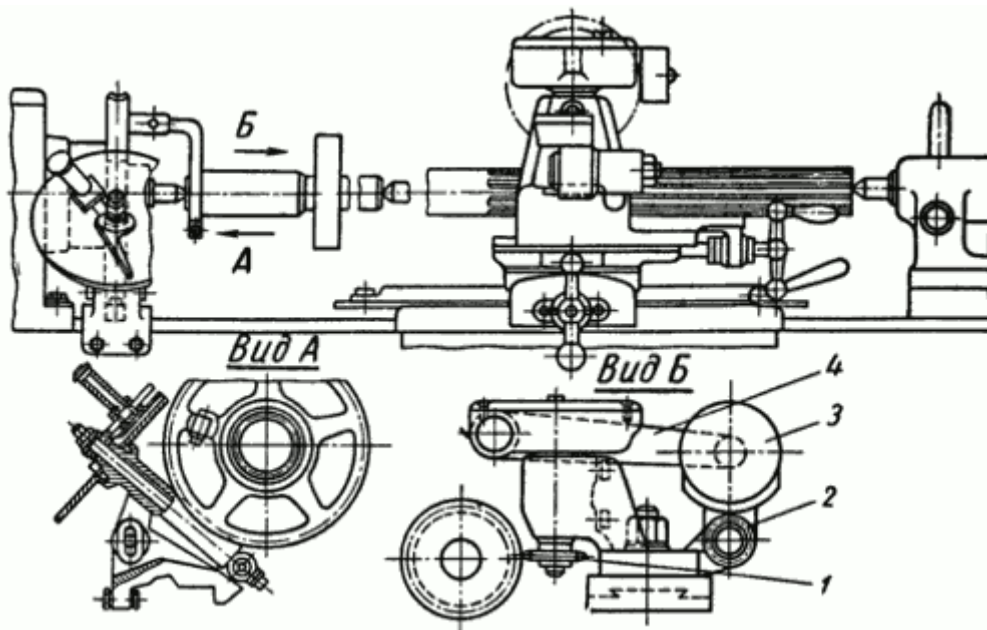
Приспособление для фрезерования зубчатых колес и шлицевых валиков.
